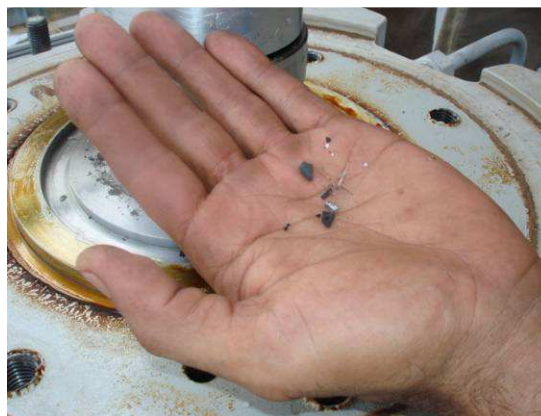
Detalhes Fragmentos – Inspeção em Campo
